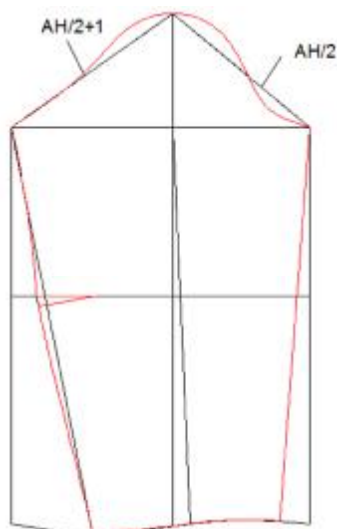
Схема чертежа БК втачного рукава для женского платья [165]:
